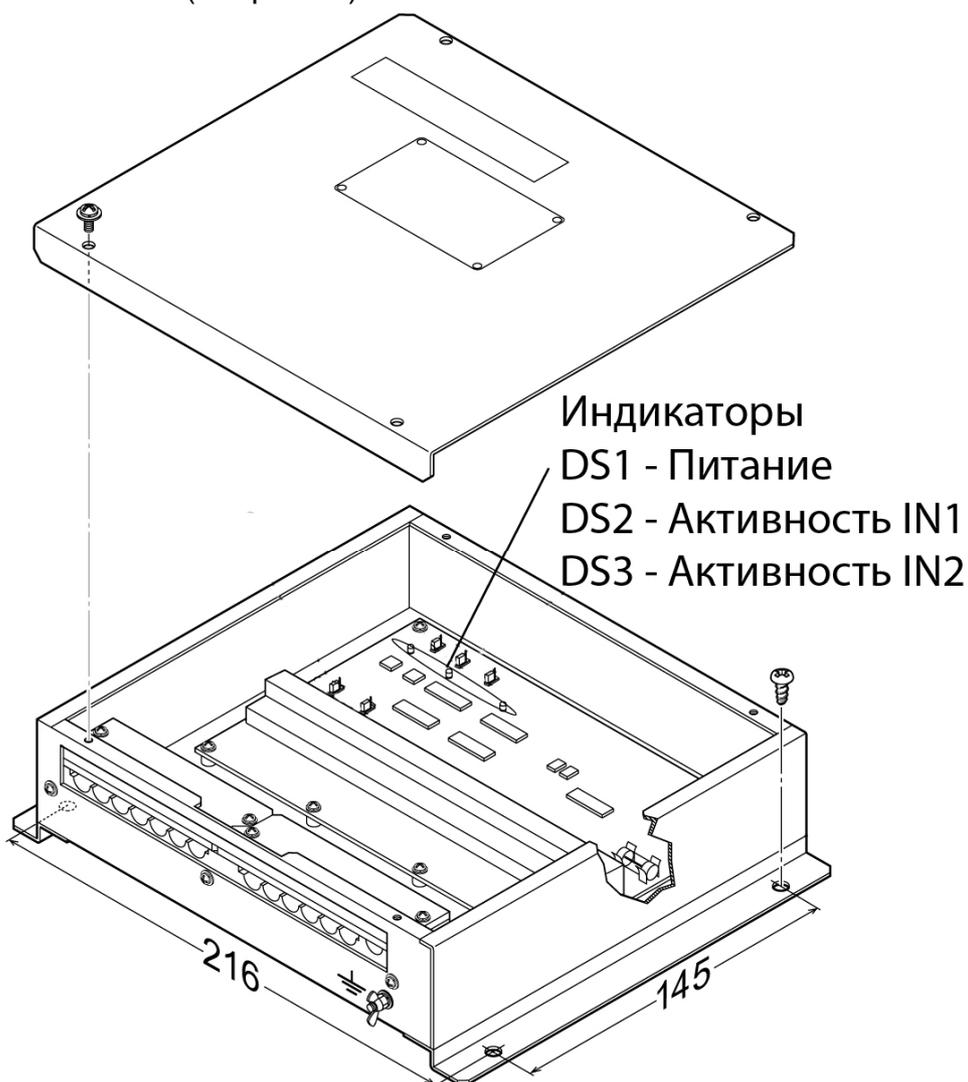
Общий вид коммутатора Beta 100 с посадочными размерами.
